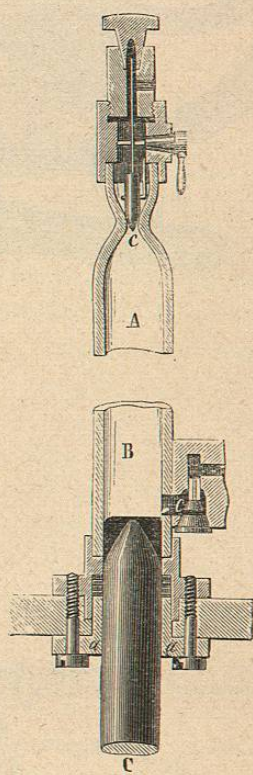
Detalles de un émbolo de la máquina de Kravogl
